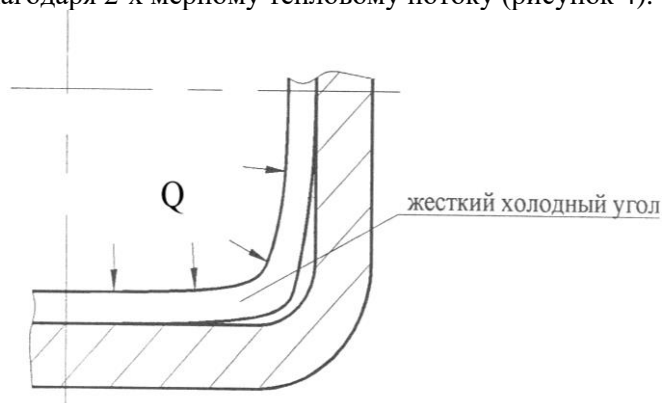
Механизм образования газового зазора в углах заготовки при ее затвердевании в гильзе кристаллизатора
